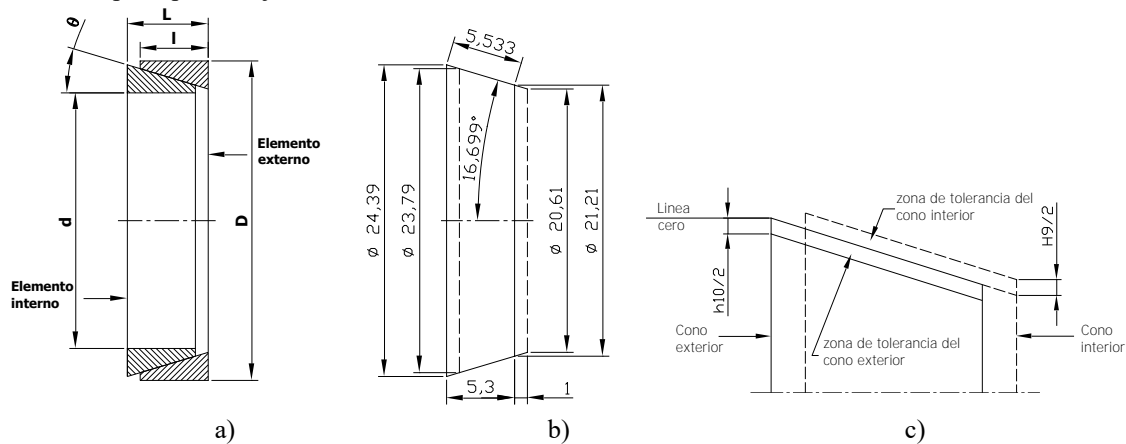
Ensamble de piezas cónicas, a) elementos cónicos nominales, b) dimensiones nominales y c) representación de las zonas de tolerancia.
